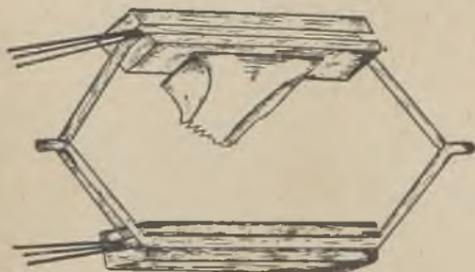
Gebrauch der Ziehholzer beim Aufziehen der Formspulen im Schraubstock.
